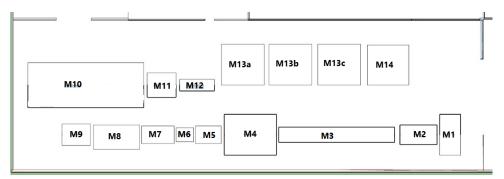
Vista en planta de las maquinarias en el área de producción.
